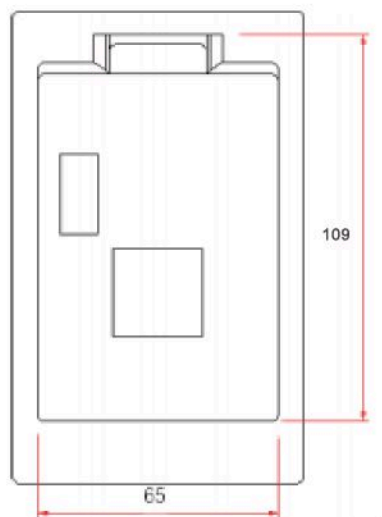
Схема габаритных и установочных размеров листовой металлической конструкции
